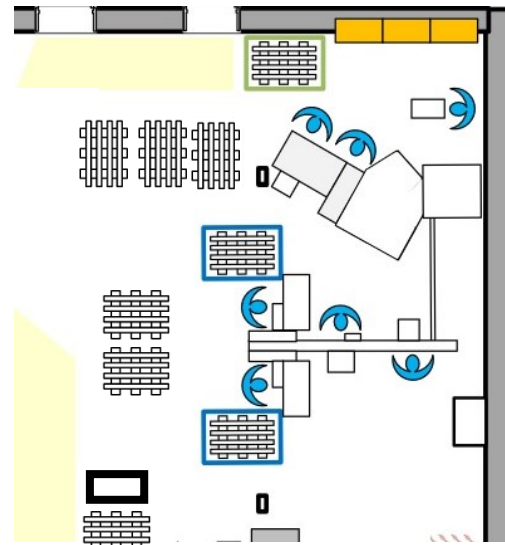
Návrh layoutu č. 1 (vlastní zpracování)
